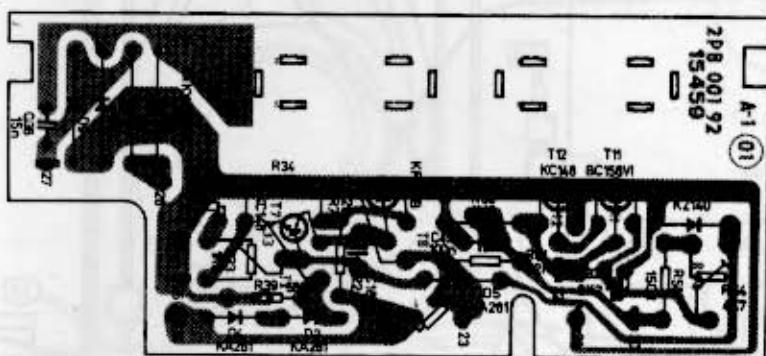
Deska zesilovačů pájená (pohled ze strany součástek)
